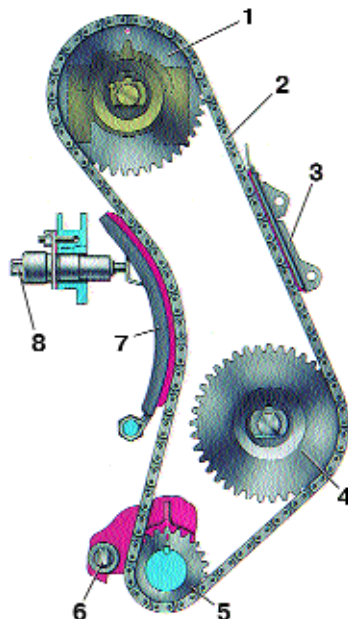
Схема механизма привода распределительного вала и вспомогательных органов двигателя мод. 2106–70: 1 – звездочка распределительного вала; 2 – цепь; 3 – успокоитель цепи; 4 – звездочка валика привода масляного насоса; 5 – звездочка коленчатого вала; 6 – ограничительный палец; 7 – башмак натяжителя; 8 – натяжитель цепи
